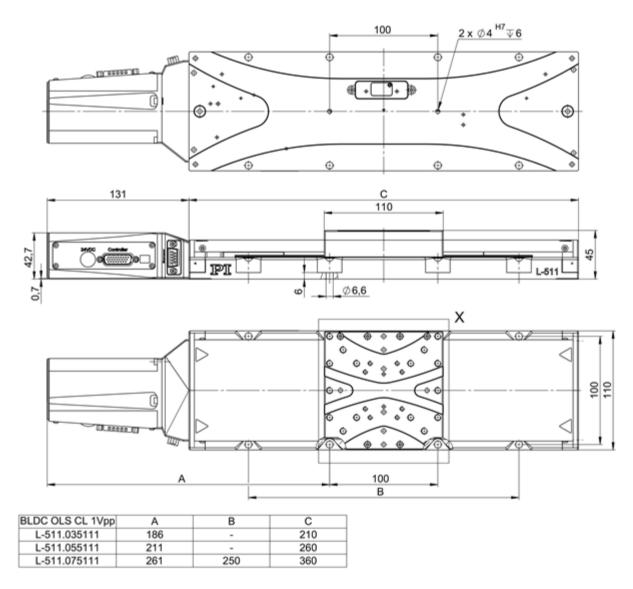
L-511-Versionen mit BLDC-Motor und Linearencoder, Abmessungen in mm
